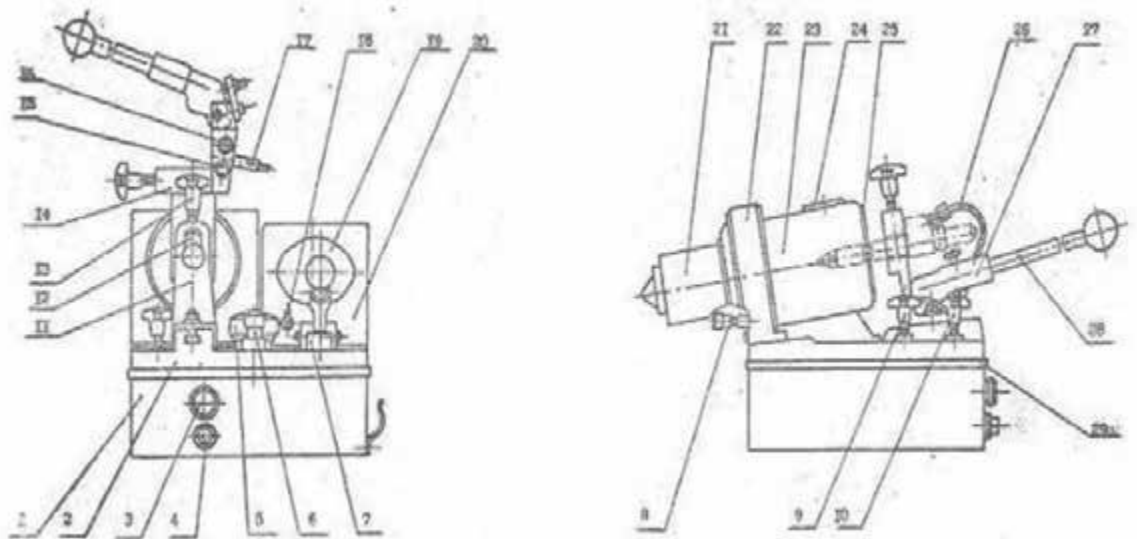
Схема стенду для перевірки форсунок: 1 – корпус; 2 – кришка; 3 – масловказівник; 4 – зливна пробка; 5 – сапун; 6 – вихідний штуцер; 7 – насос; 8 – вставка; 9 – кран; 10 - кран "злив"; 11 – кронштейн; 12 – призма; 13 – гвинт натискний; 14 – затискач насос-форсунки; 15 – ковпачок; 16 – штуцер; 17 – паблон; 18 – тумблер; 19 – манометр; 20 – кожух; 21 - електродвигун ME-236; 22 – вентилятор; 23 - камера упорскування; 24 - заглушка; 25 – кришка; 26 – змінний паливопровід; 27 – важіль; 28 – рукоятка; 29 – прокладка
